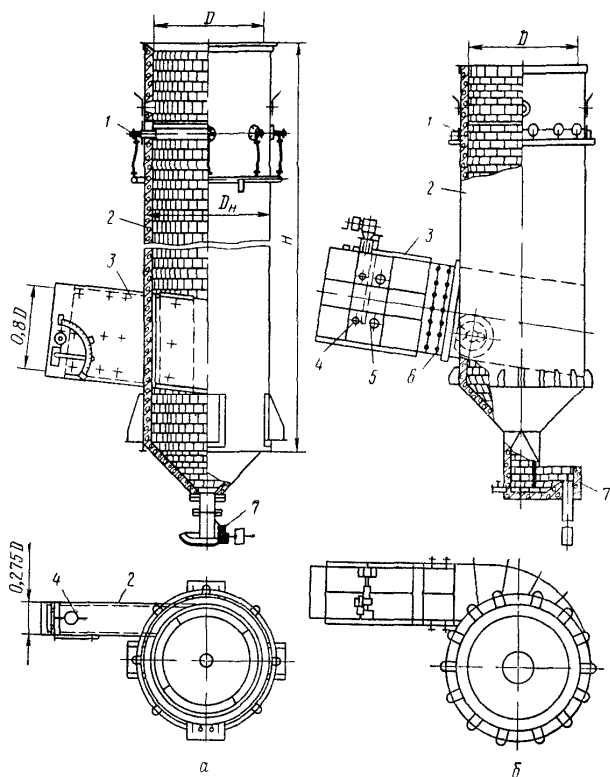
Центробежные скрубберы: а – ЦС-ВТИ; б – МП-ВТИ: 1 – оросительные сопла; 2 – корпус; 3 – входной патрубок; 4 – смывные сопла; 5 – оросительные сопла прутковой решетки; 6 – прутковая решетка; 7 – гидрозатвор
